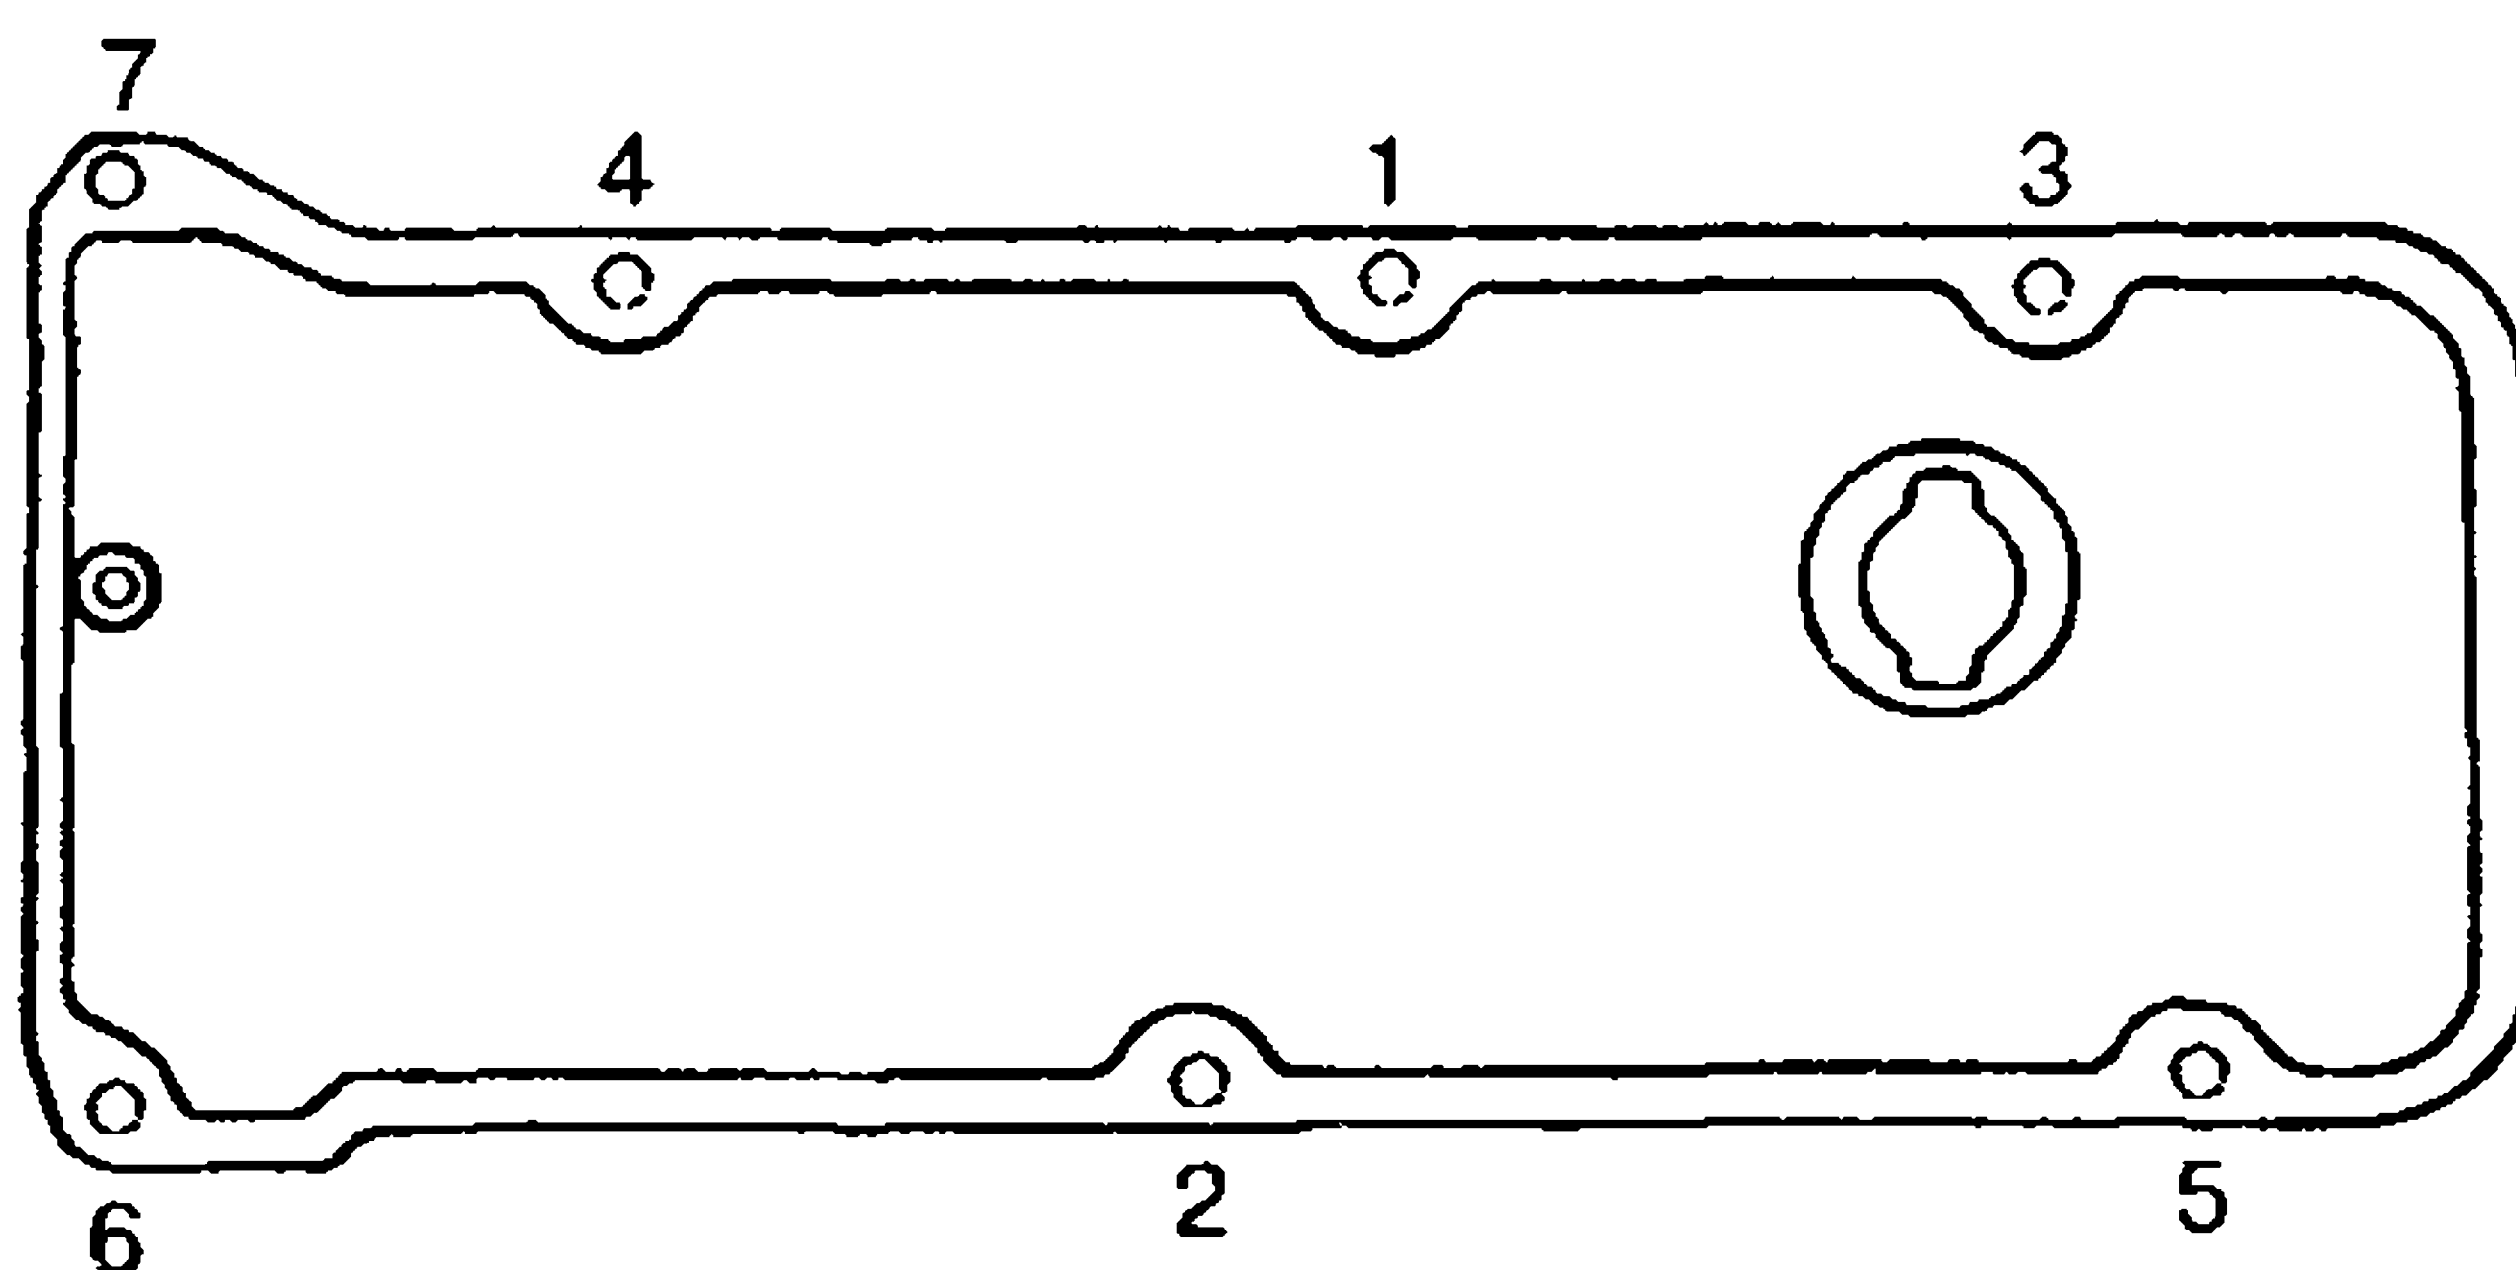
Последовательность затяжки гаек крышки головки цилиндров
